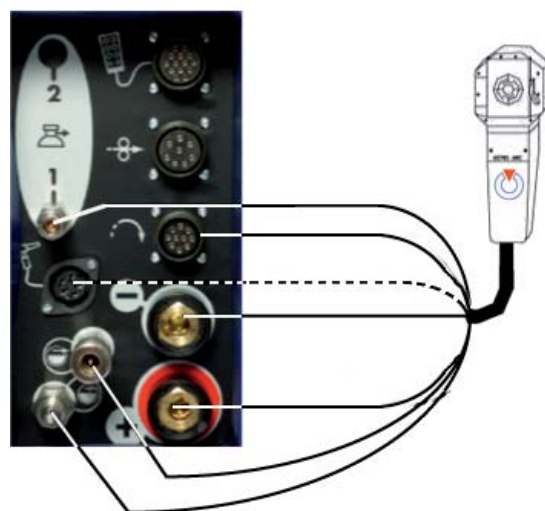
Anschluss eines geschlossenen, flüssigkeitsgekühlten Schweißkopfes (--- für die Köpfe mit integrierten Steuerungen)
